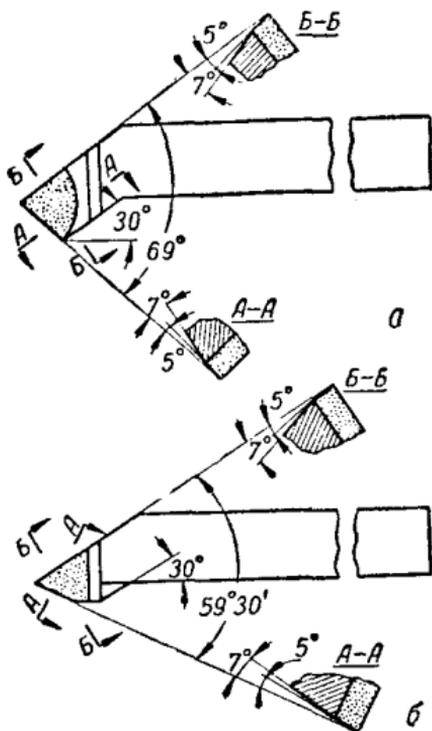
Резьбовые резцы конструкции токаря В. М. Бирюкова:
